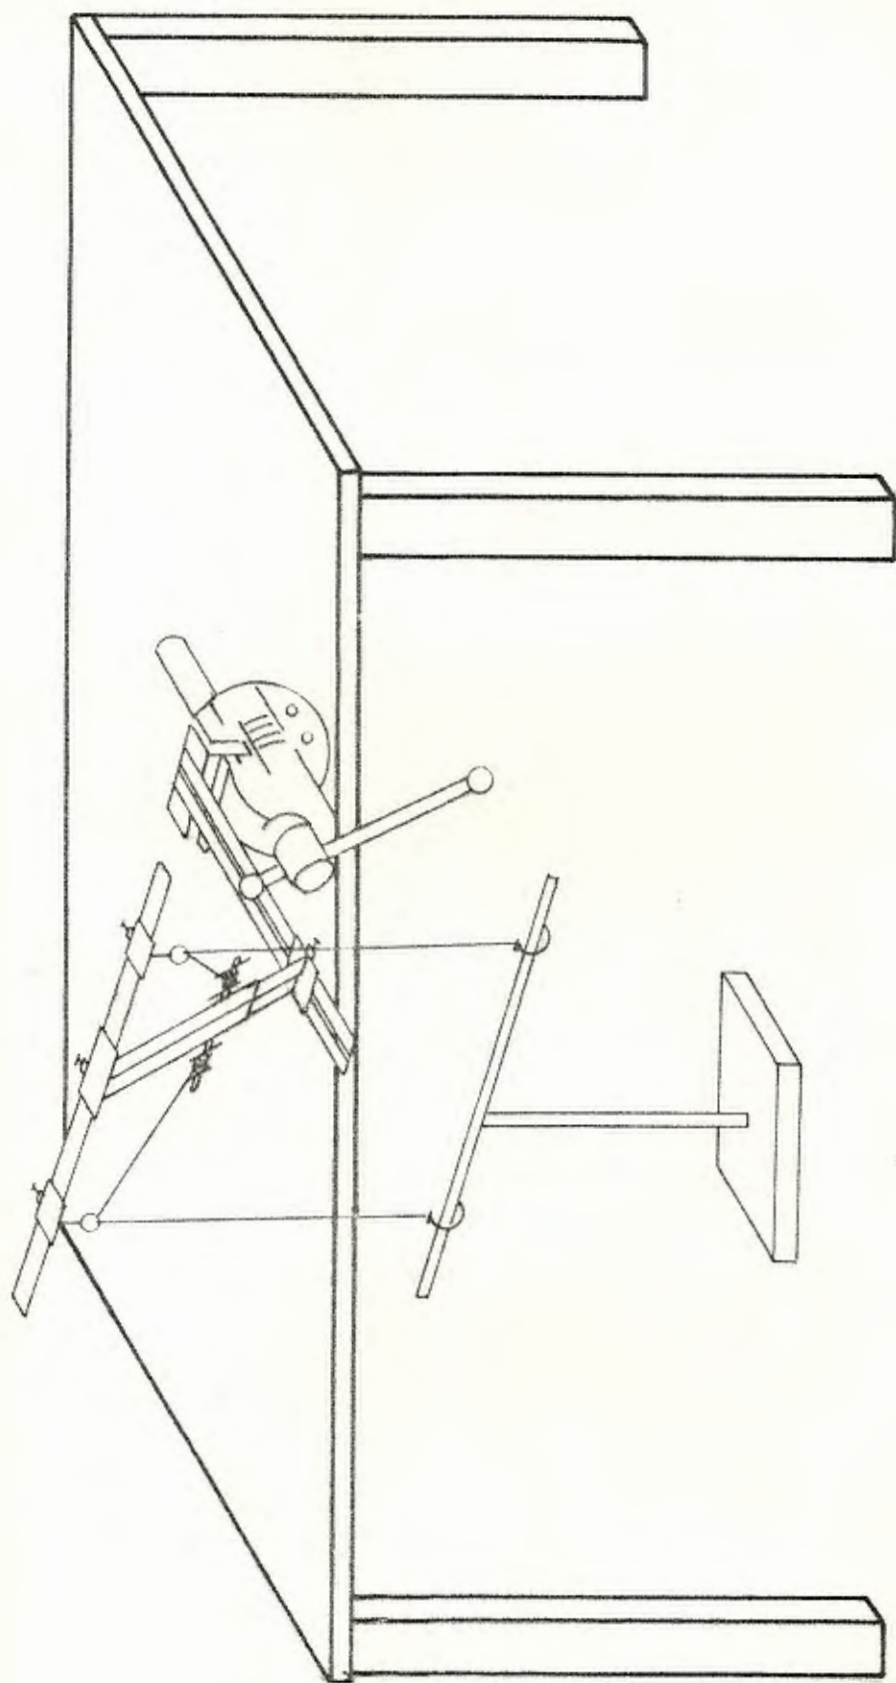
UTIL PARA SOSTENER PIEZAS A SOLDAR
